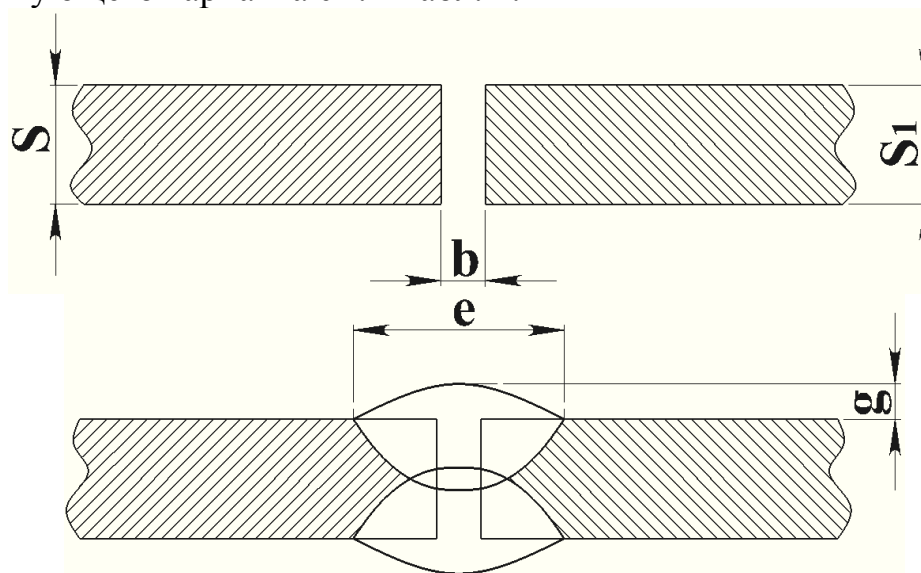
Стыковой сварной шов ГОСТ 5264–80–С7
